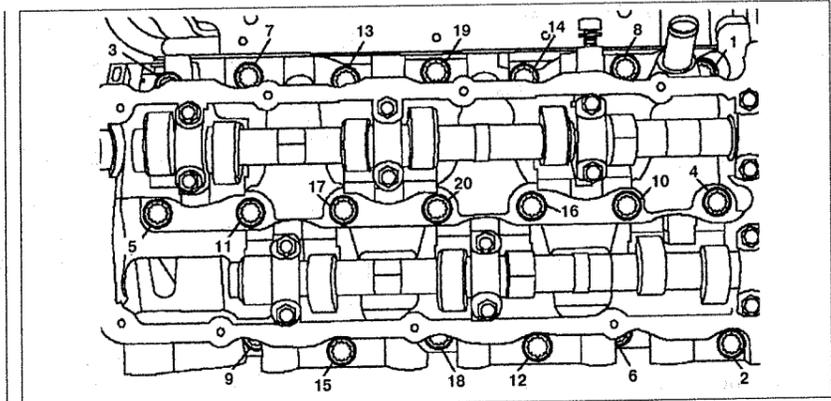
Порядок затяжки болтов головки блока цилиндров.
